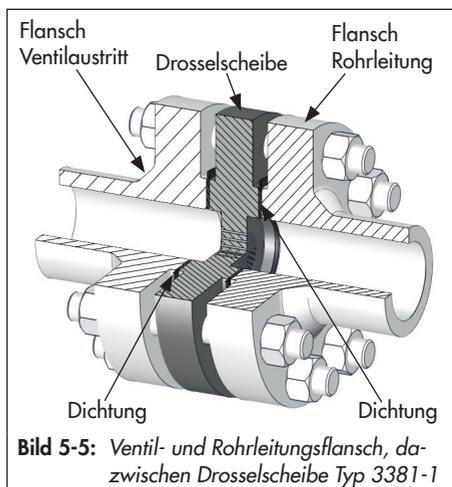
Ventil- und Rohrleitungsflansch, dazwischen Drosselscheibe Typ 3381-1
